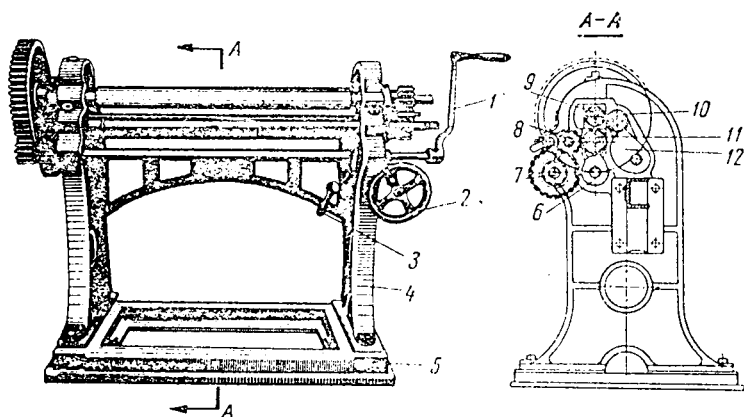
Листогибочный трехвалковый станок с ручным приводом
